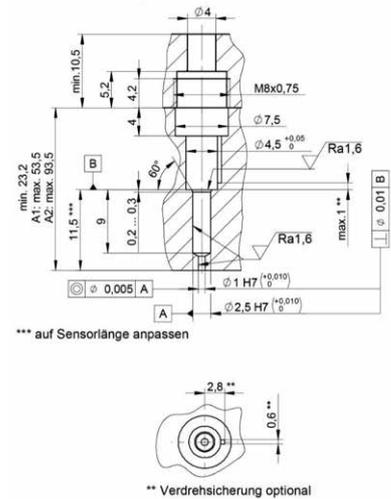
Montagebohrung für Einbau mit ladungsführender Distanzhülse
